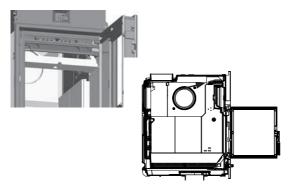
Pose de la pierre avant (H4-09) sur la pierre latérale bas comme représenté, la soulever sous la plaque de recouvrement, puis la pousser contre l'arrière de la paroi avant en fonte et la déposer sur le coffre à air.
